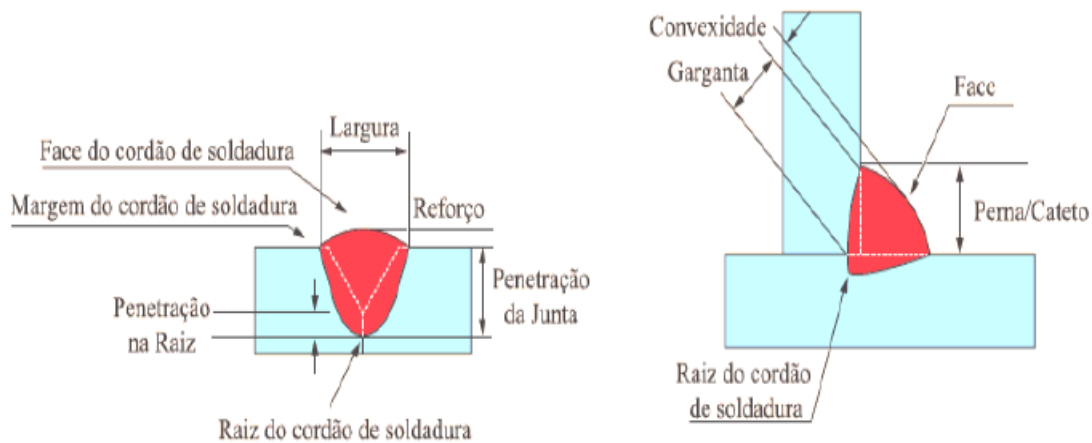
Nomenclatura relacionada com a geometria dos cordões de soldadura (Silva F. J., 2016)
